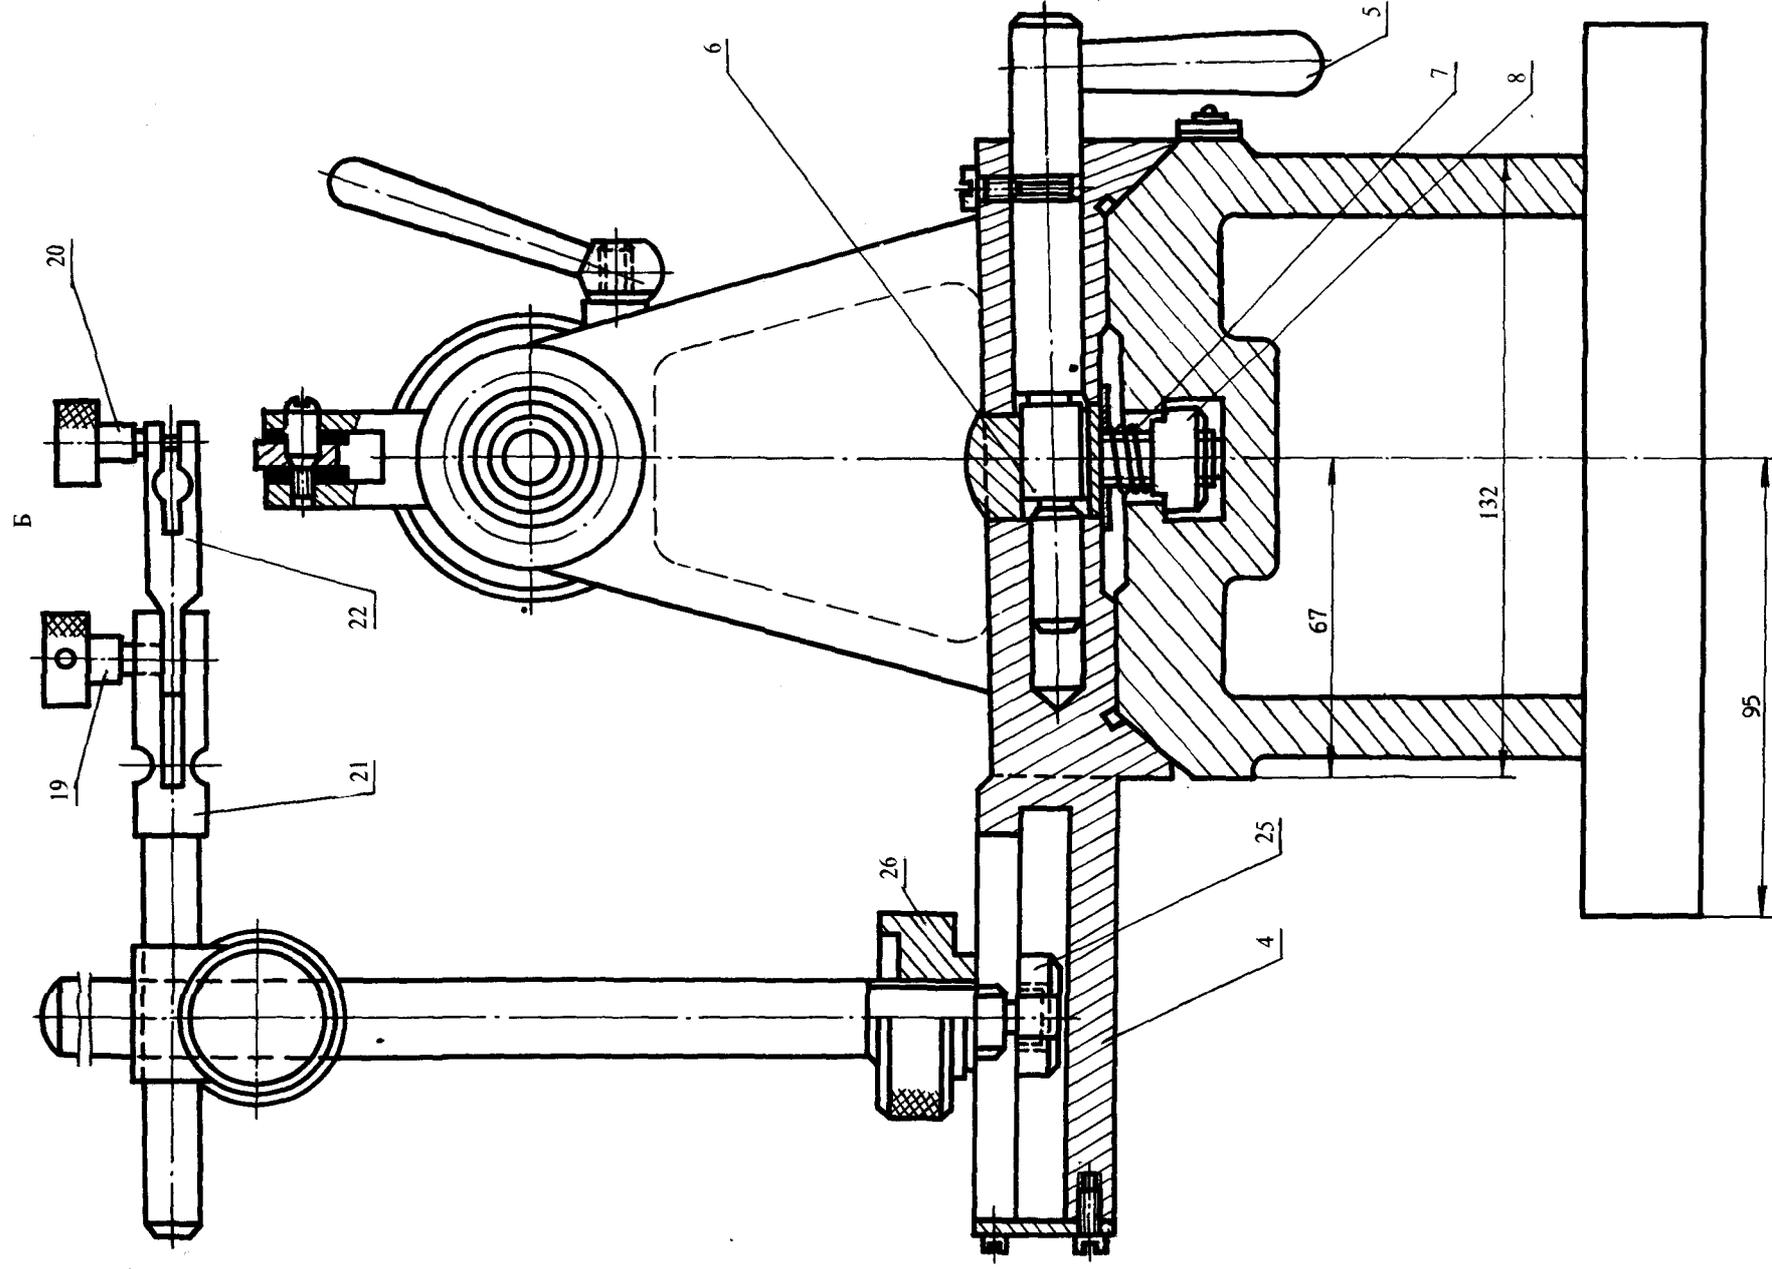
Универсальное приспособление для контроля валов (вид Б на рис. 3.29):
